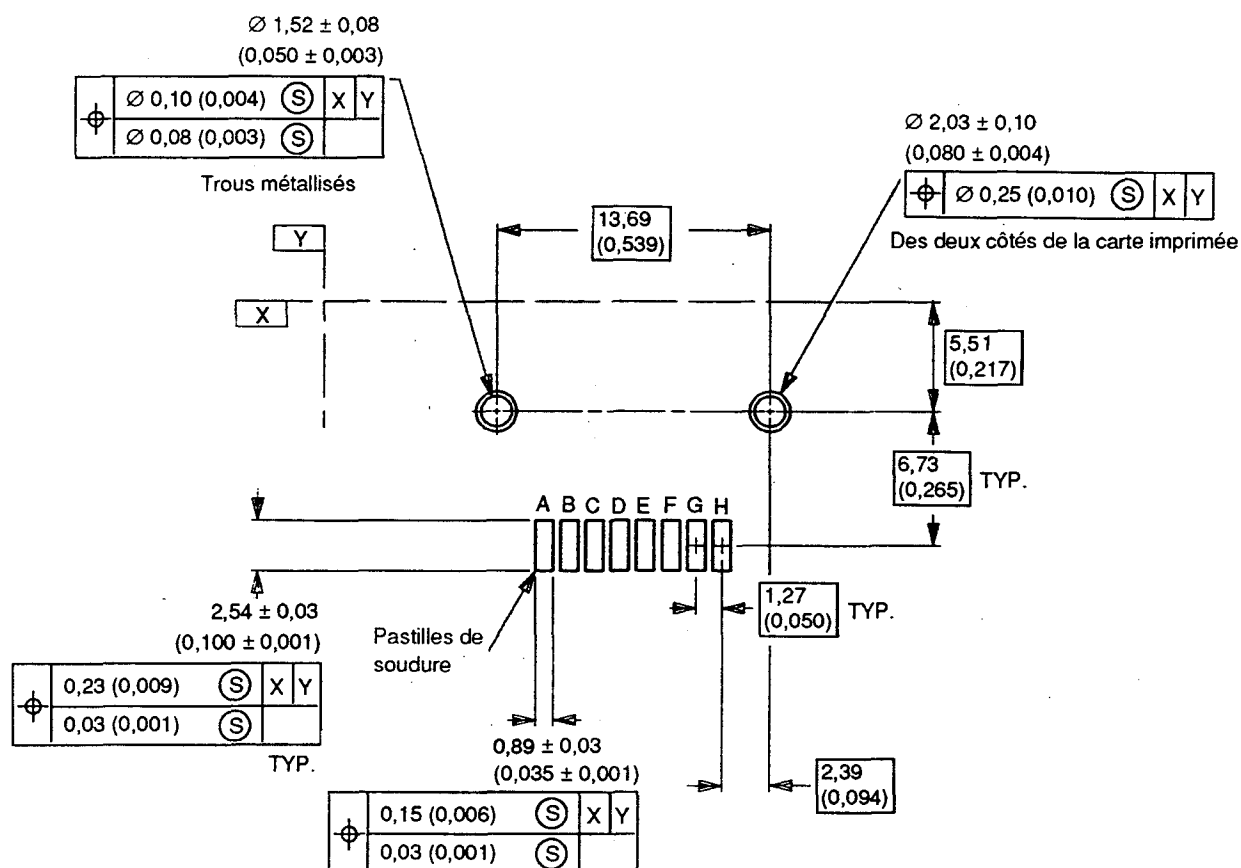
Grille d'implantation des pastilles de soudure pour les embases à montage en surface
